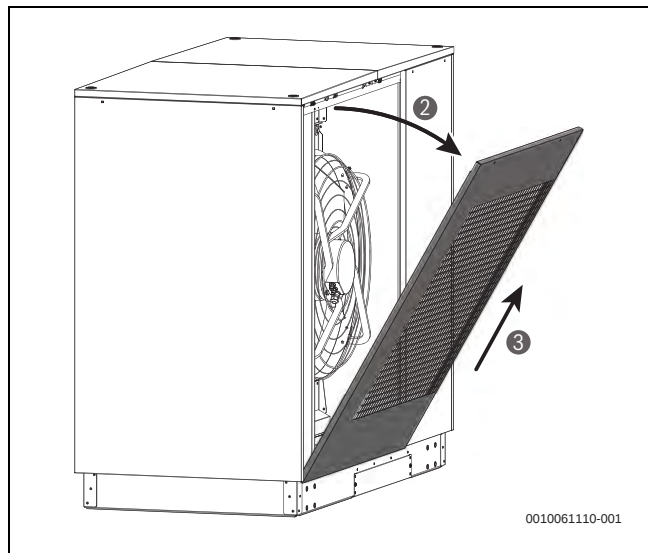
Gitterblech aus dem Sockelblech entfernen.
